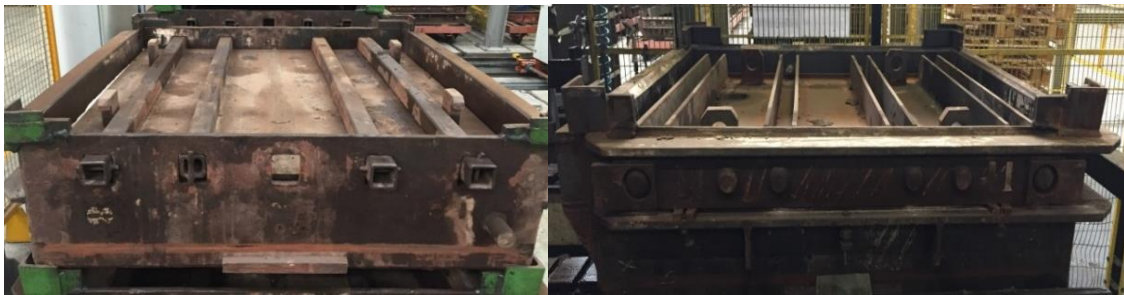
Molde de cavilhas (esquerda) e molde automático (direita)
